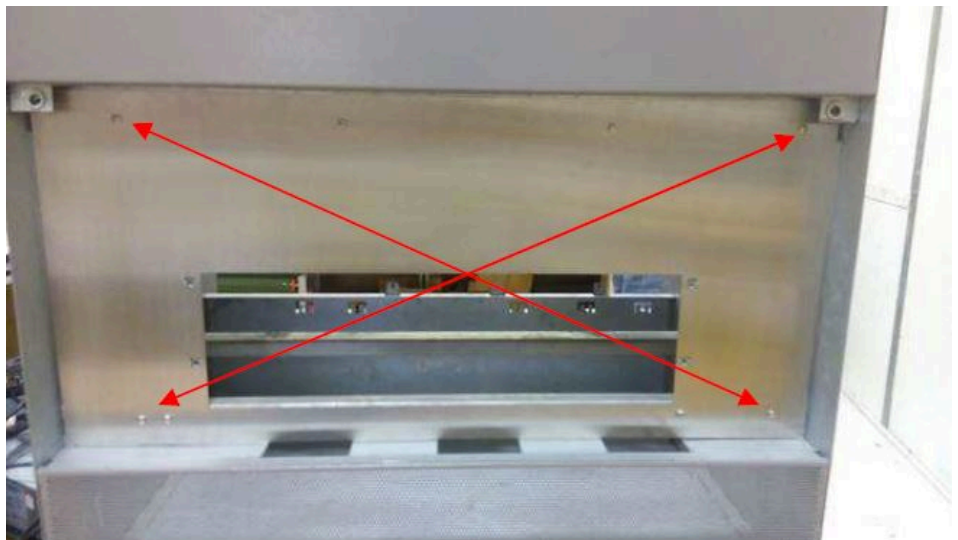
Kit C39165-A7080-B176-1 - Composants à utiliser à l'arrière
